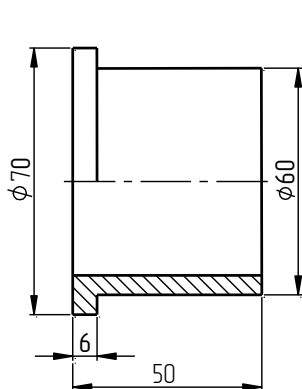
Размеры, указываемые на рабочем чертеже детали – втулки (не указан диаметр ее внутренней поверхности, содержащей *притупку* для последующей обработки после сборки)
